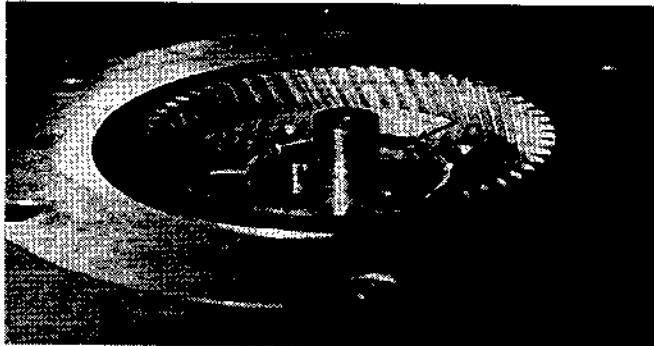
Литьевая форма для зубчатых колес газораспределения
